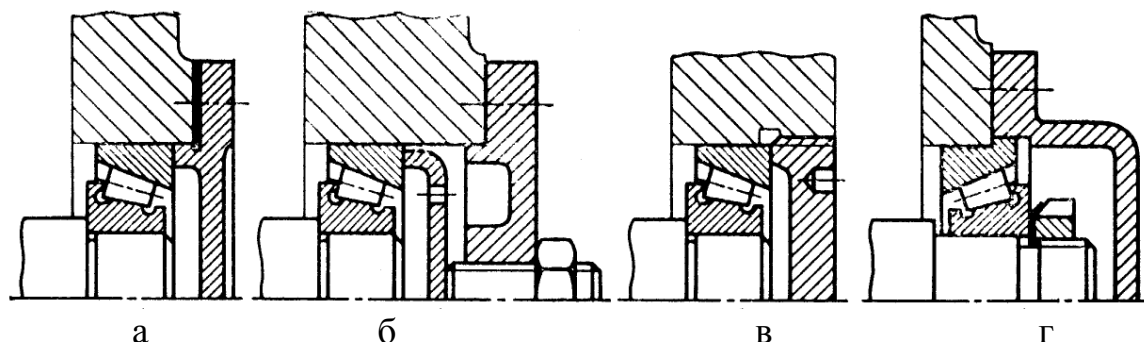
Способы регулирования зазора в конических роликоподшипниках: а – с помощью прокладки; б– регулировочным винтом; в и г – регулировочной гайкой.
